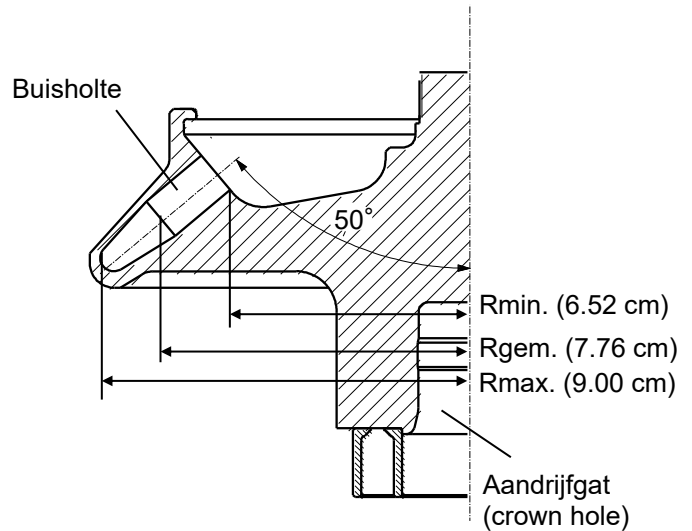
Dwarsdoorsnede P50A3 rotor
